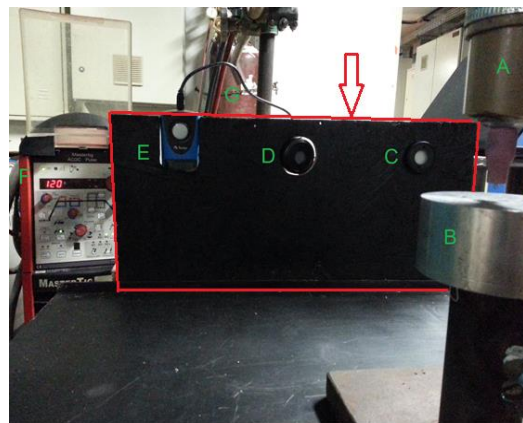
Montagem e Posicionamento dos Sensores de Medição. A - Tocha TIG refrigerada a água; B - Bloco de Alumínio; C - Sensor UVC; D - Sensor UVA e UVB; E - Luxímetro; F - Fonte de Soldagem; G - Balão de argônio.
